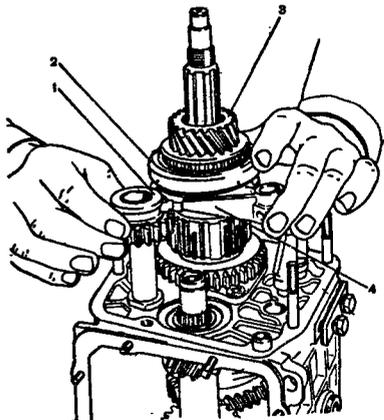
Снятие промежуточной шестерни заднего хода, шестерни V передачи в сборе с синхронизатором и вилкой: 1 - промежуточная шестерня заднего хода; 2 - муфта включения V передачи; 3 - шестерня V передачи с синхронизатором; 4 - вилка включения V передачи и заднего хода
